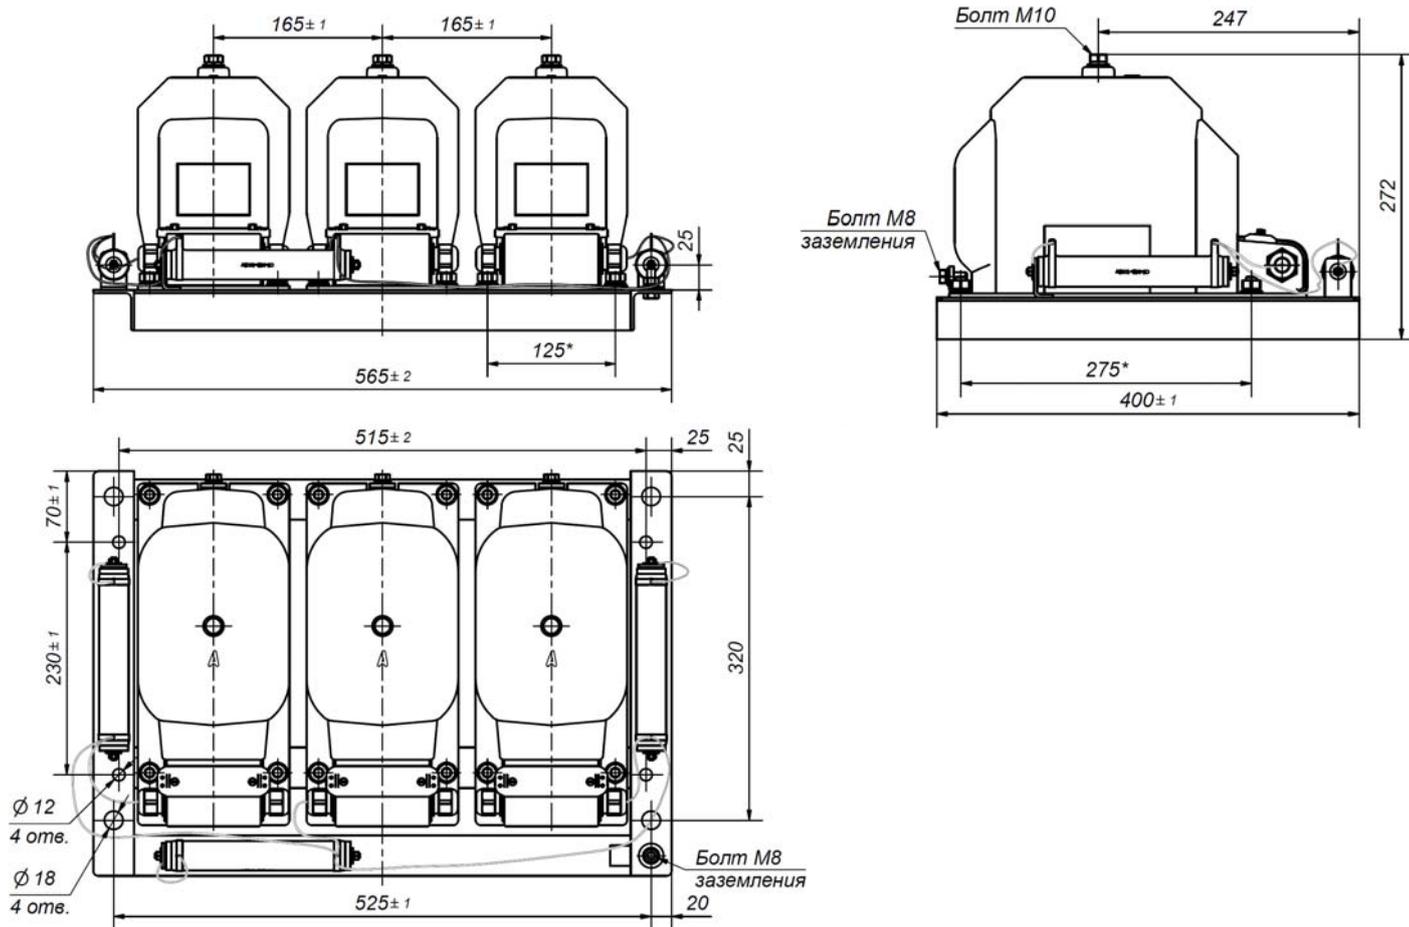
Габаритный чертеж Группы 3×IVS1...
